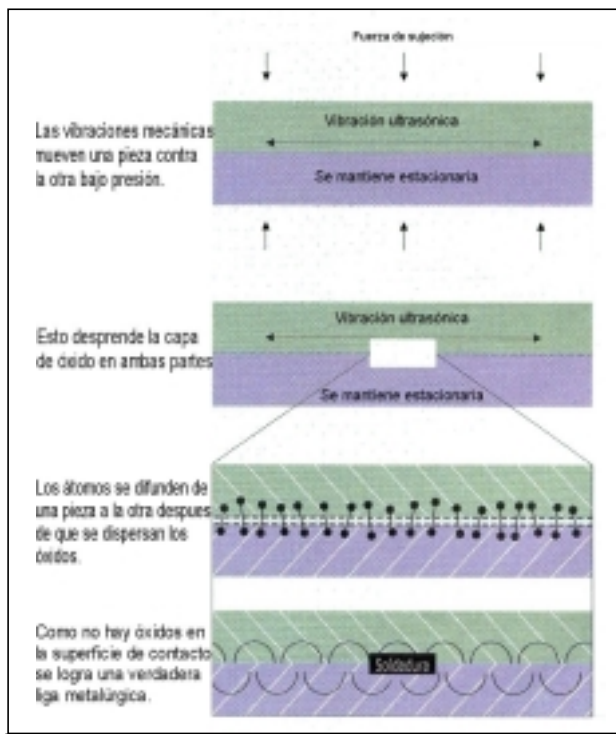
Proceso de soldadura ultrasónica de metales
